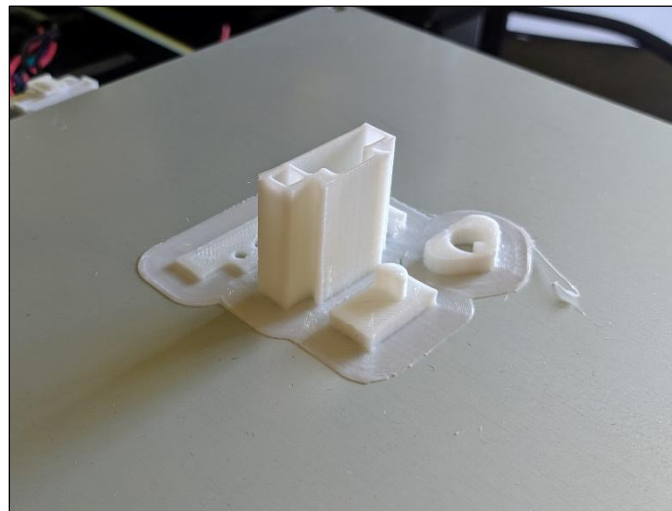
Pieza Rotating Gauntlet impresa con soporte
